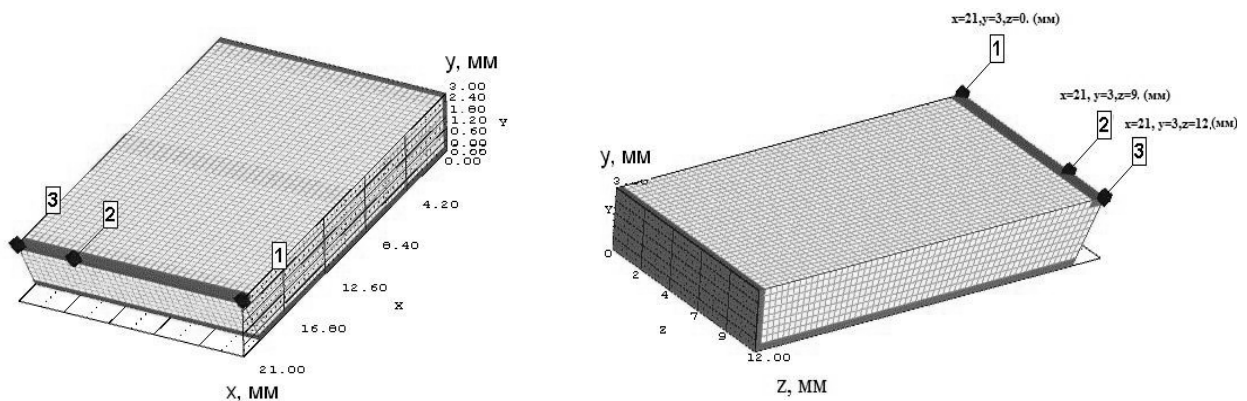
Розрахункова модель твердосплавної пластини, що заточується
